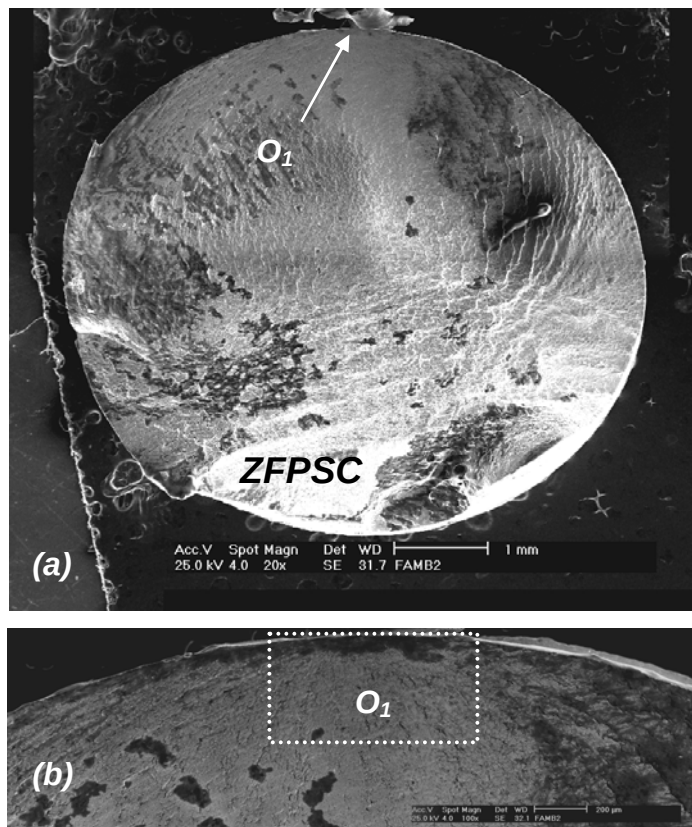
Superficie de fractura del material base a 650 MPa.
